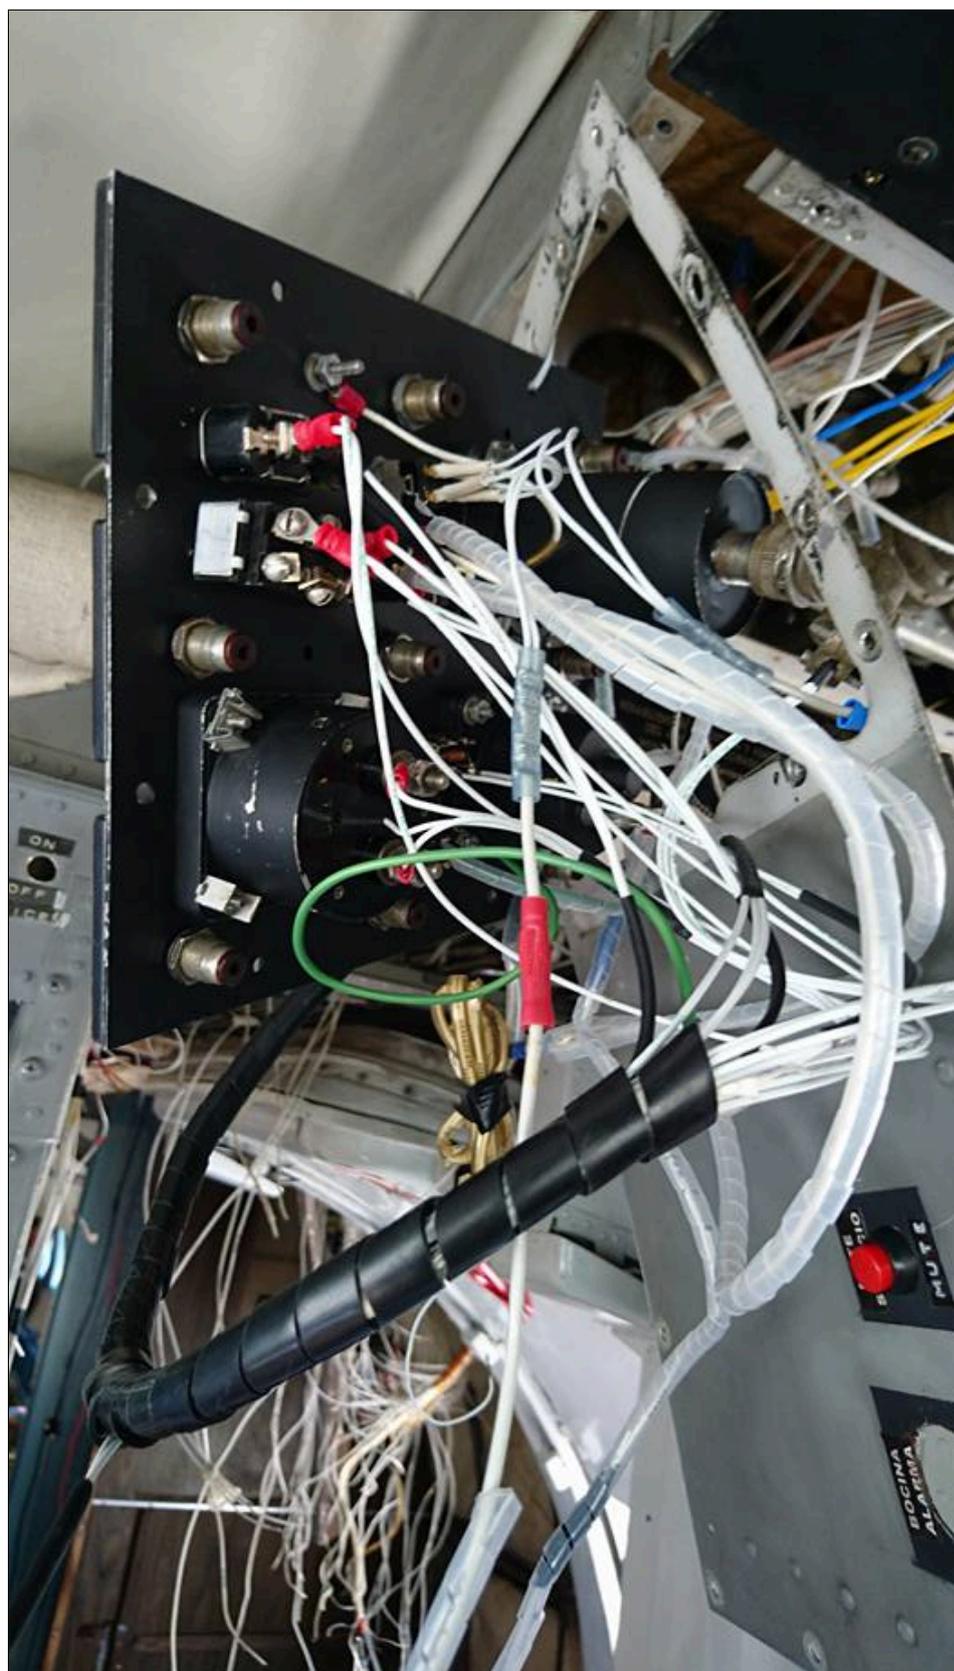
Enrutamiento de cables hasta el panel del APU desde la caja de control.
